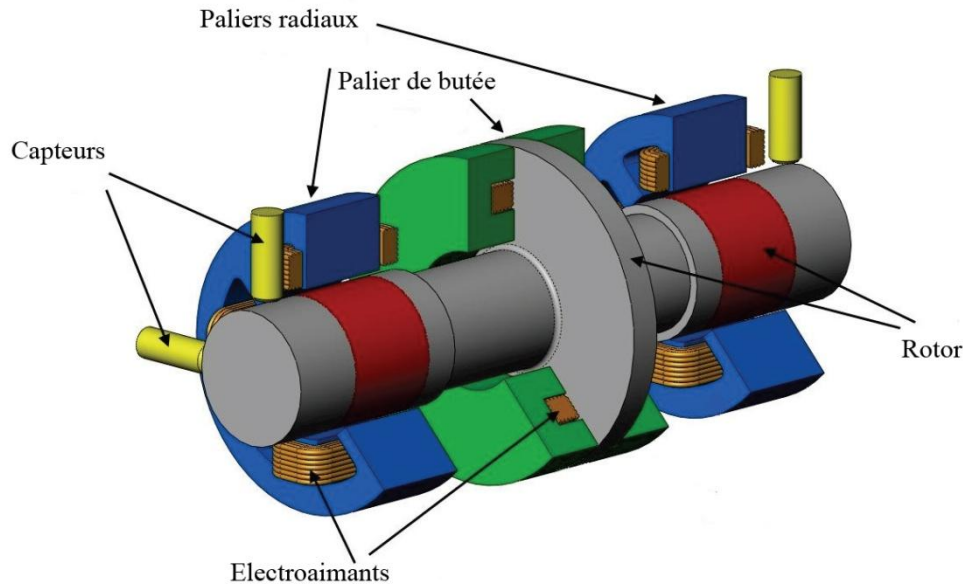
Rotor supporté par des paliers magnétiques [9].
